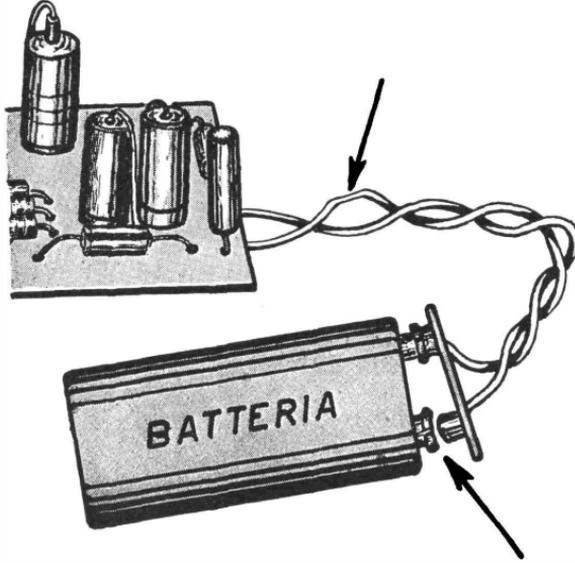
Batteria staccata o collegamento spezzato.
